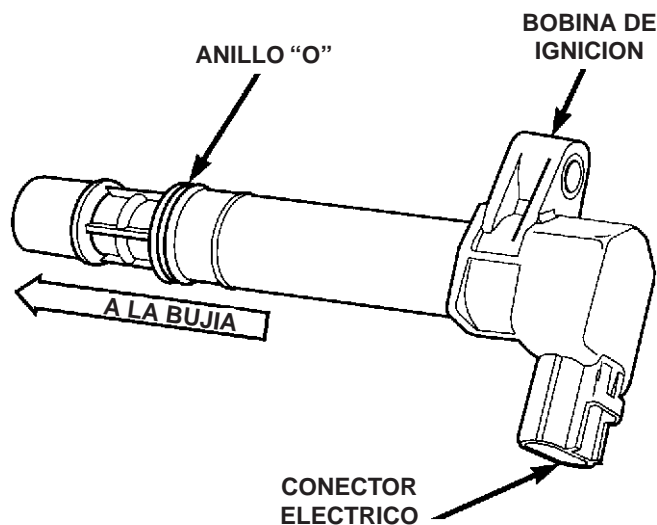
Bobina de ignición del motor V-8 de 4.7 L
